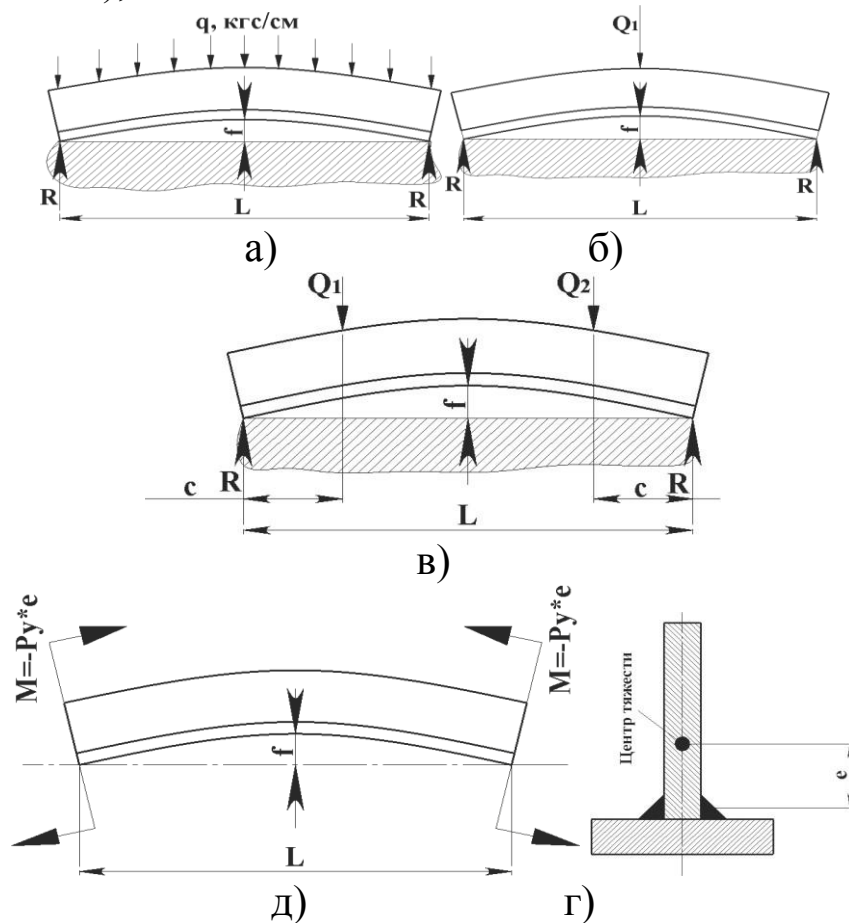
Продольная деформация сварной балки и схемы ее нагружения в сборочно–сварочном кондукторе:
